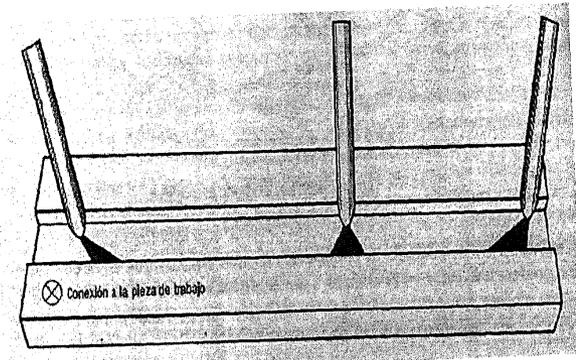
Fenómeno del soplo de arco: el goteo de soldadura no cae parejo sino ladeado. Deja una soldadura dispareja, salpicada y con poca penetración.
